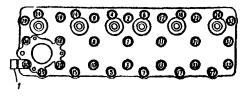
Порядок ватяжки гаек головки цилиндров и установка скобы крепления сливного шланга из испарителя автомобилей ГАЗ-52-07 № ГАЗ-52-08
